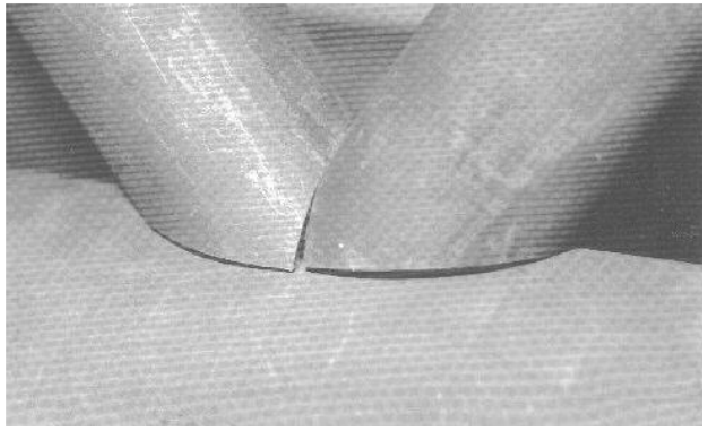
Nudo fabricado por aserrado de corte plano antes de soldar
